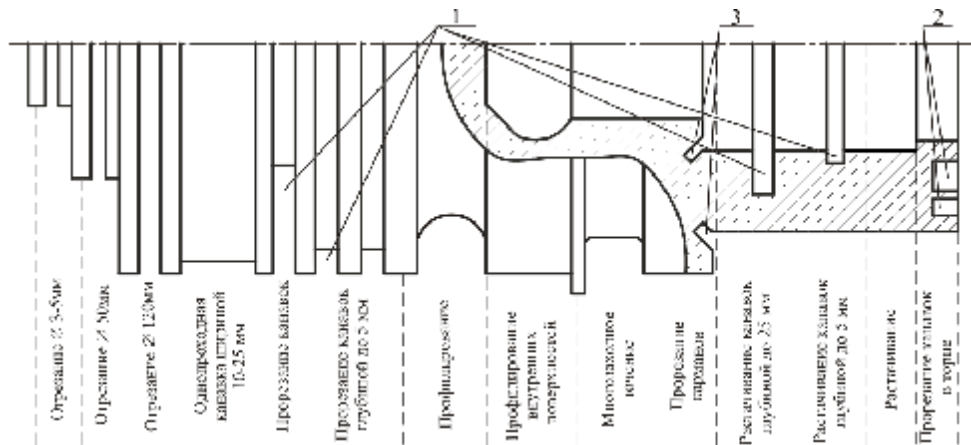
Комплексная деталь с обрабатываемыми канавками
